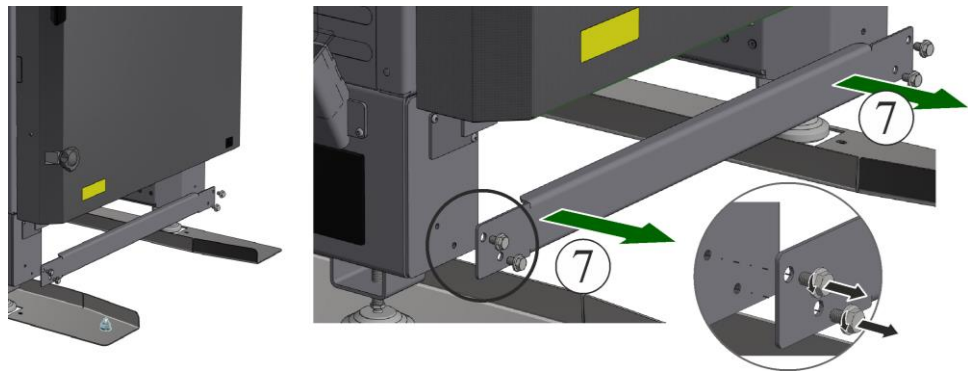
Удаление транспортировочной штанги (рисунок примерный)
